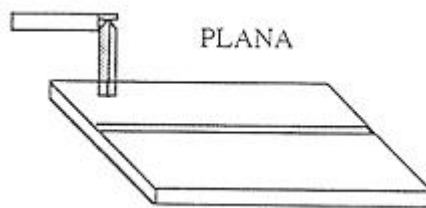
Proceso de soldadura Gtaw [12]
